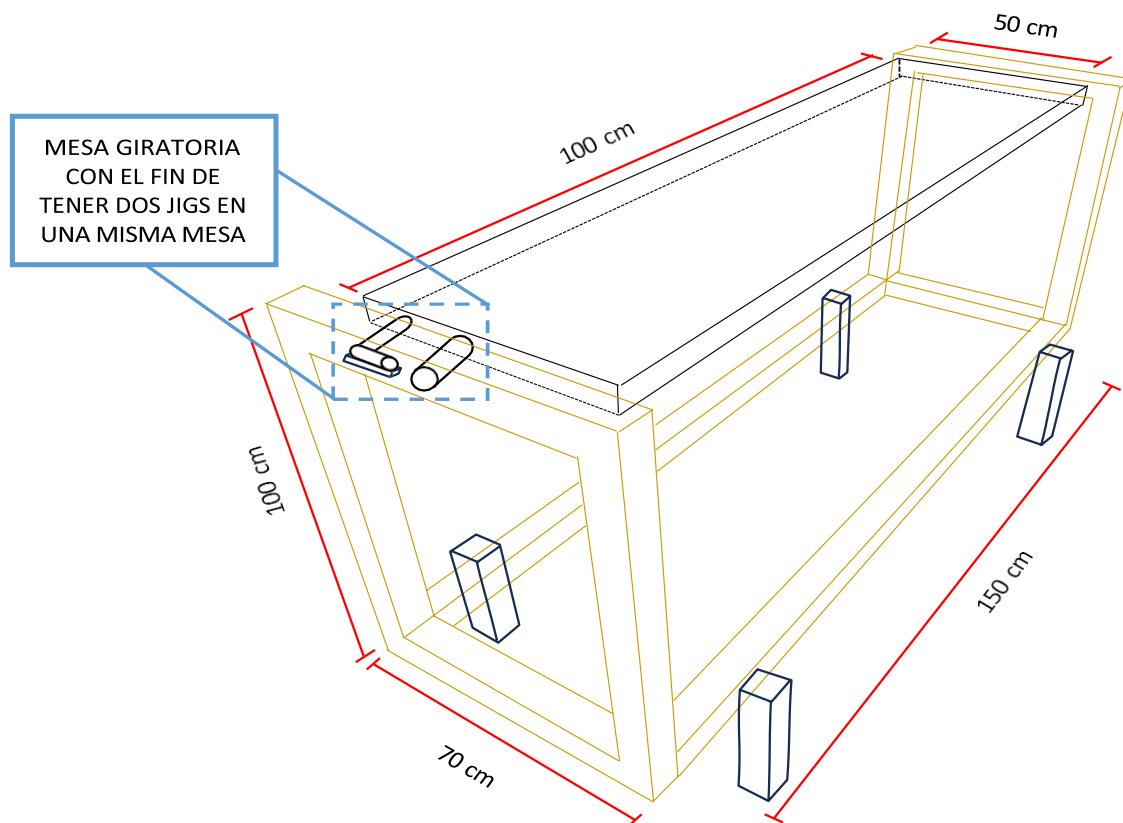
Mesa para montajes de Jig de inspección. Fuente: YMEX 2024
